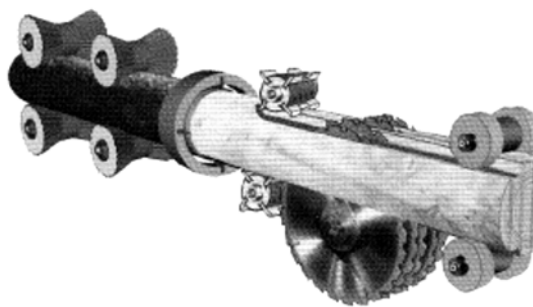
Схема работы фрезерно-профилирующего агрегата
